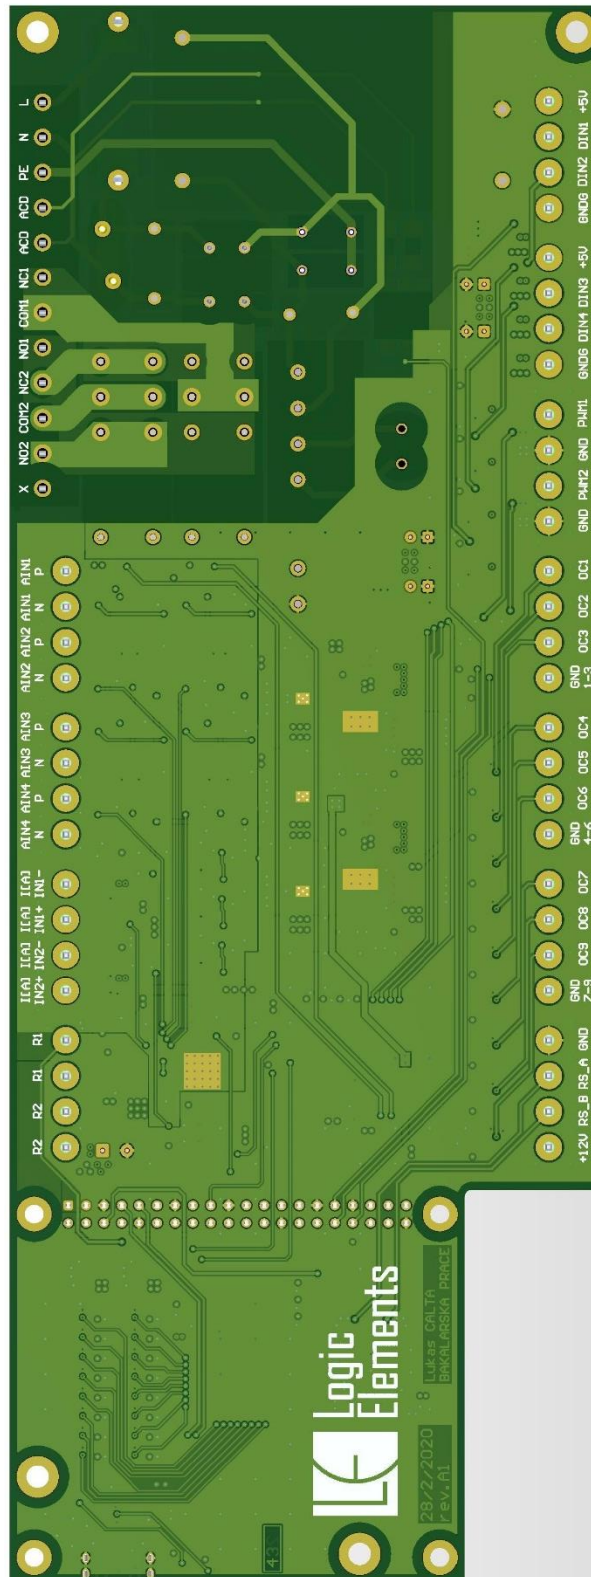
Deska plošných spojů Testing boardu – spodní vrstva mědi „BOT“
